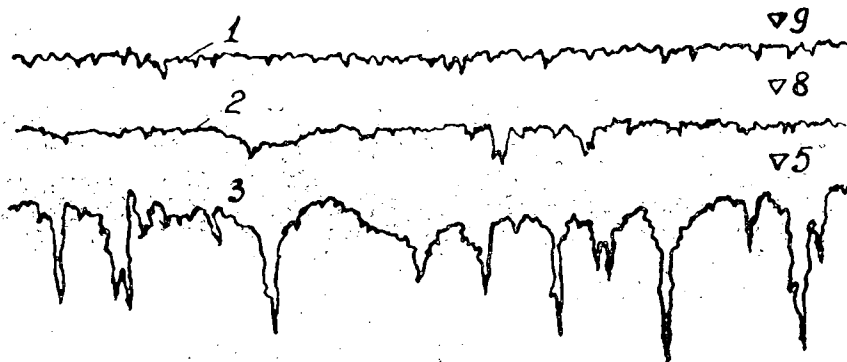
Профилограммы поверхностей деталей подшипников качения с различными видами изнашивания.
